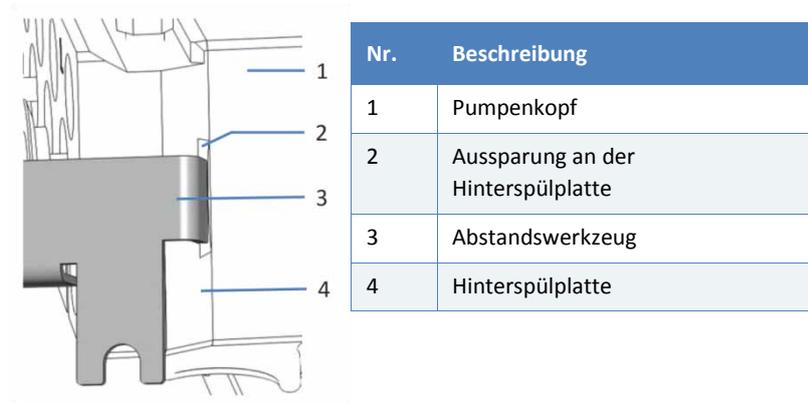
Entfernen der Hinterspülplatte mit dem Abstandswerkzeug
